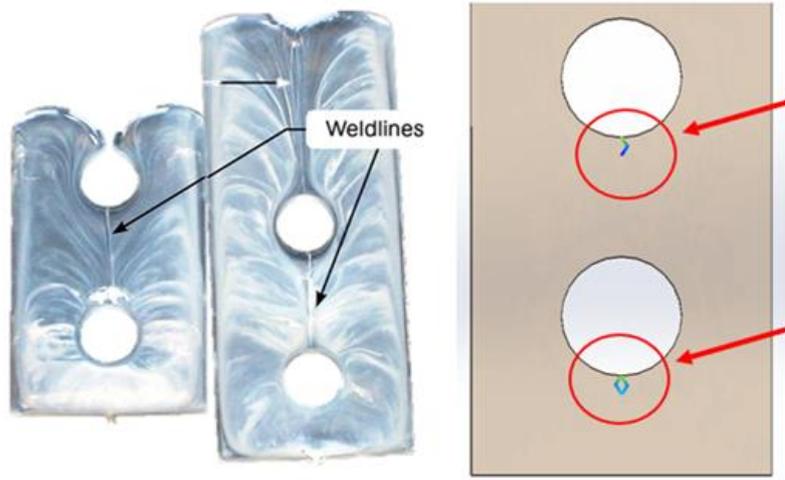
Líneas de soldadura. (Fuente: [8])
